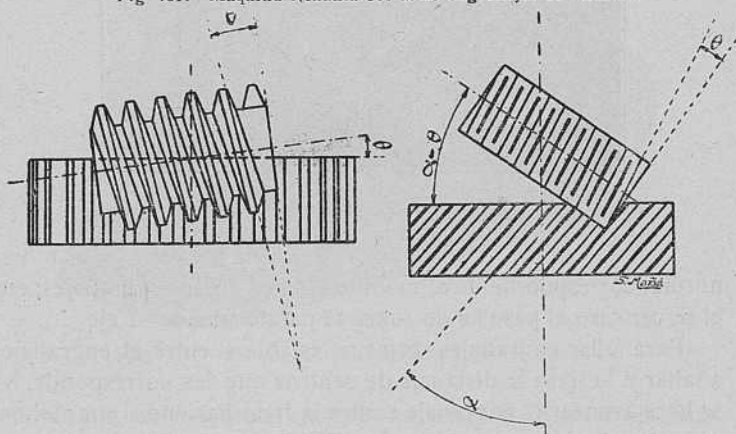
Inclinación del visinfín fresa al construir engranajes rectos o helicoidales.
